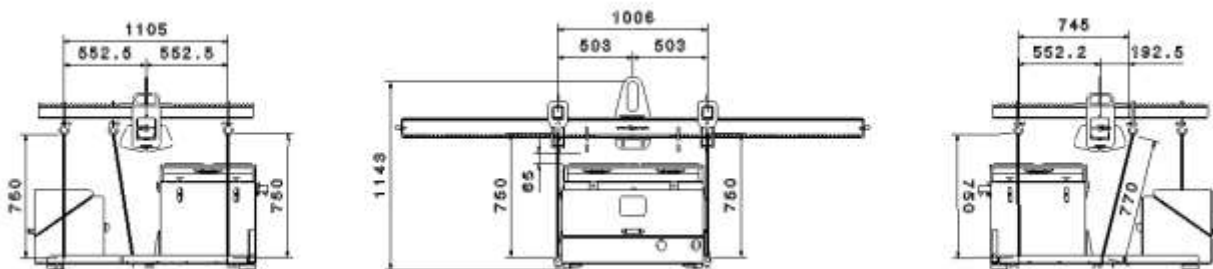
ELEVAÇÃO DE UMA CAIXA DE EQUIPAMENTO
